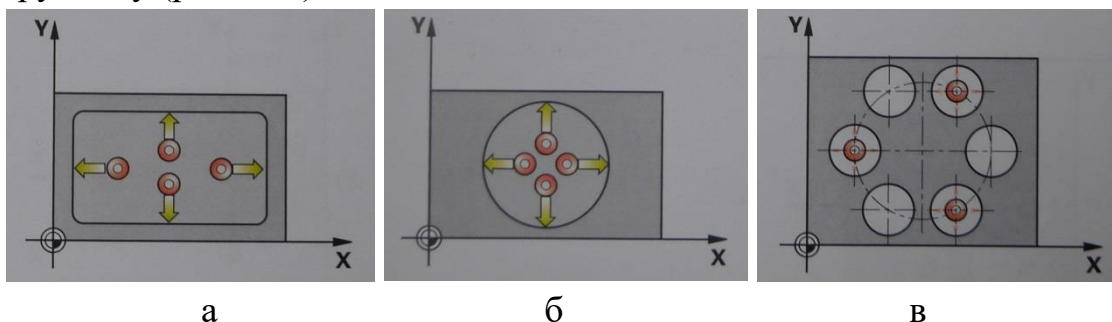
Приклади вимірювання розмірів заготовок на верстаті: а –прямокутної кишені; б – круглої кишені; в – отворів по колу
